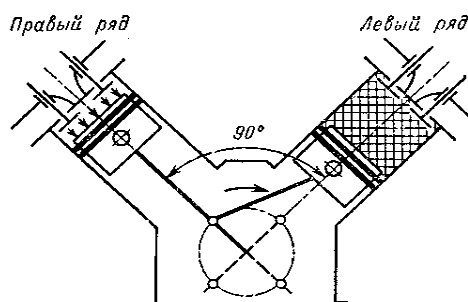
Схема кривошипно-шатунного механизма V-образного двигателя
